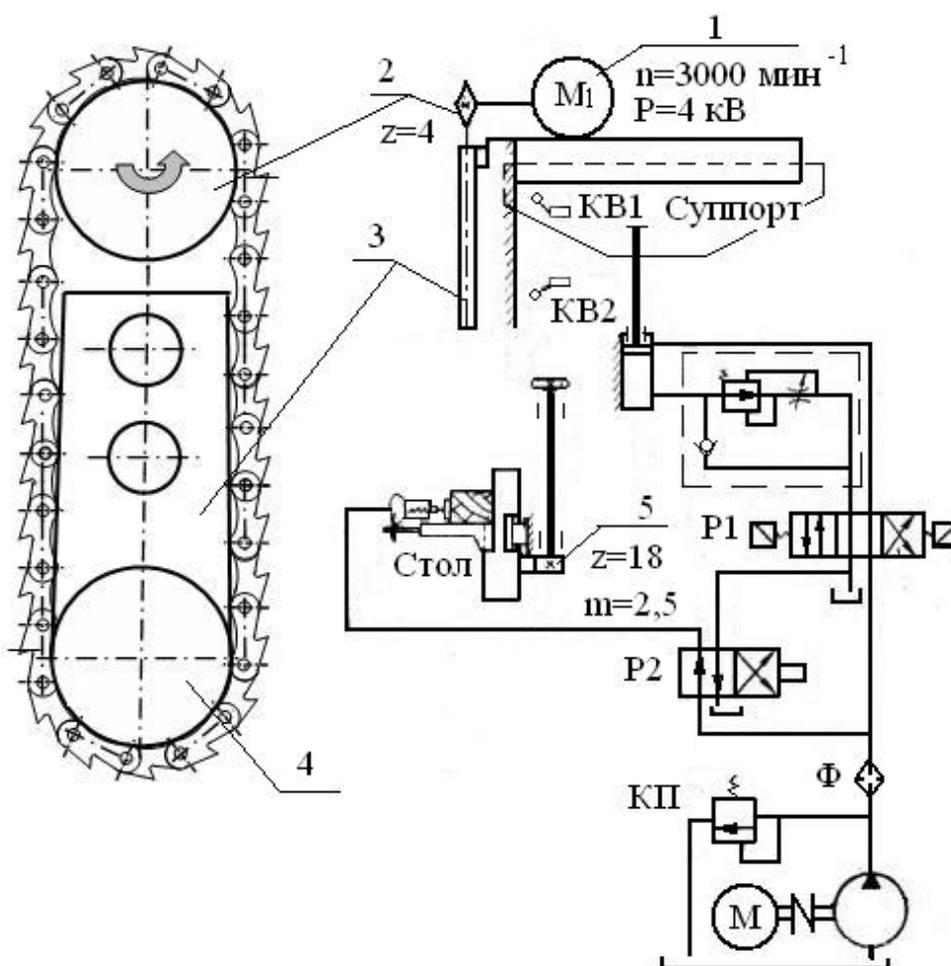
Гидрокинематическая схема цепнодолбежного станка ДЦА-2
